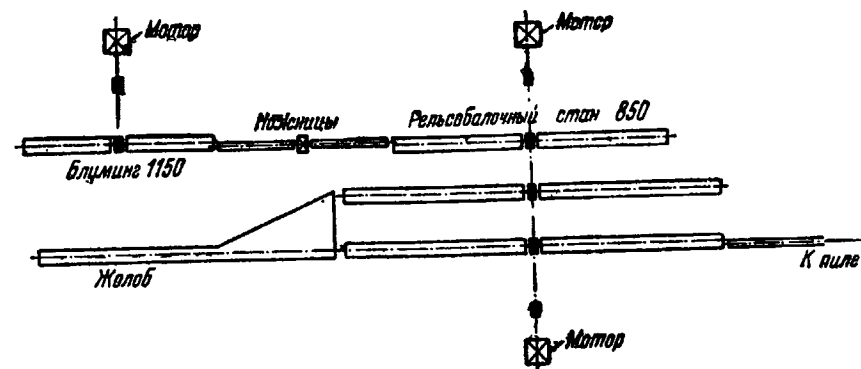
Реверсивный рельсобалочный стан 850 с двумя двигателями
